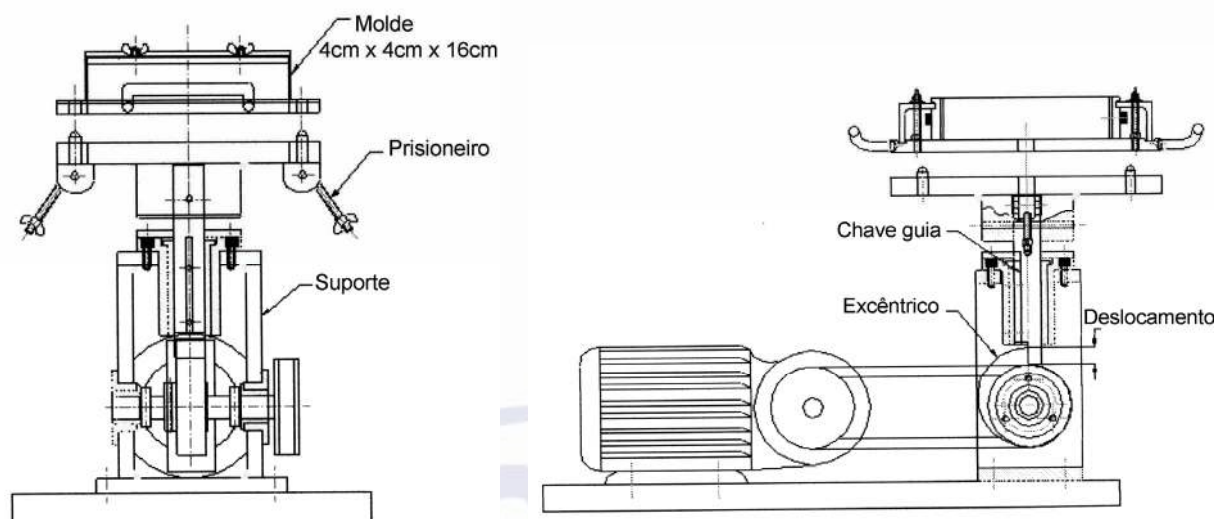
Equipamento para moldagem dos corpos-de-prova
